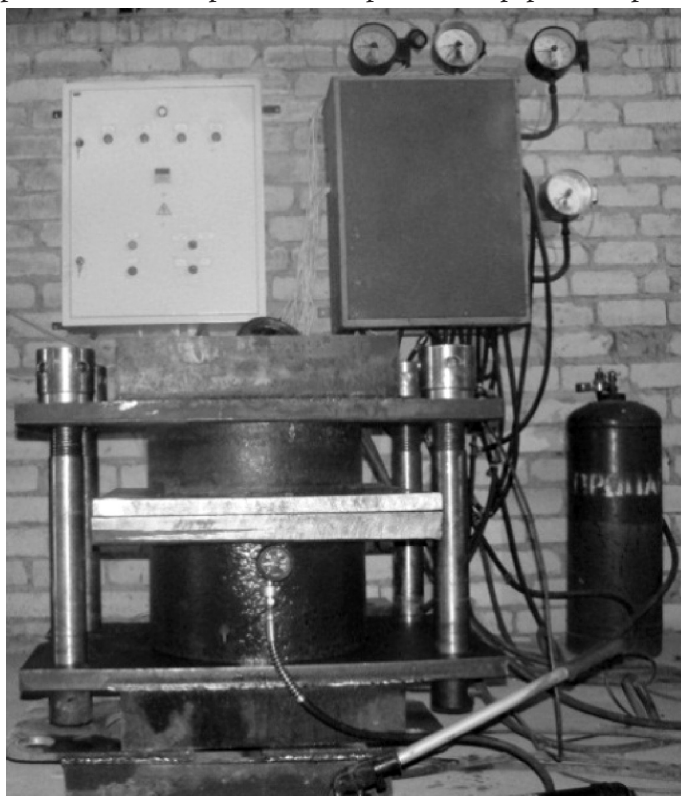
Фотография экспериментальной установки для газовой штамповки
